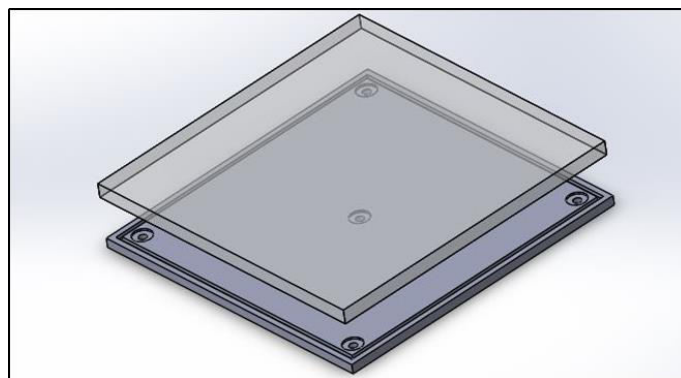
Molde RTM com orifício central (inlet) e quatro furos passantes (outlets).
